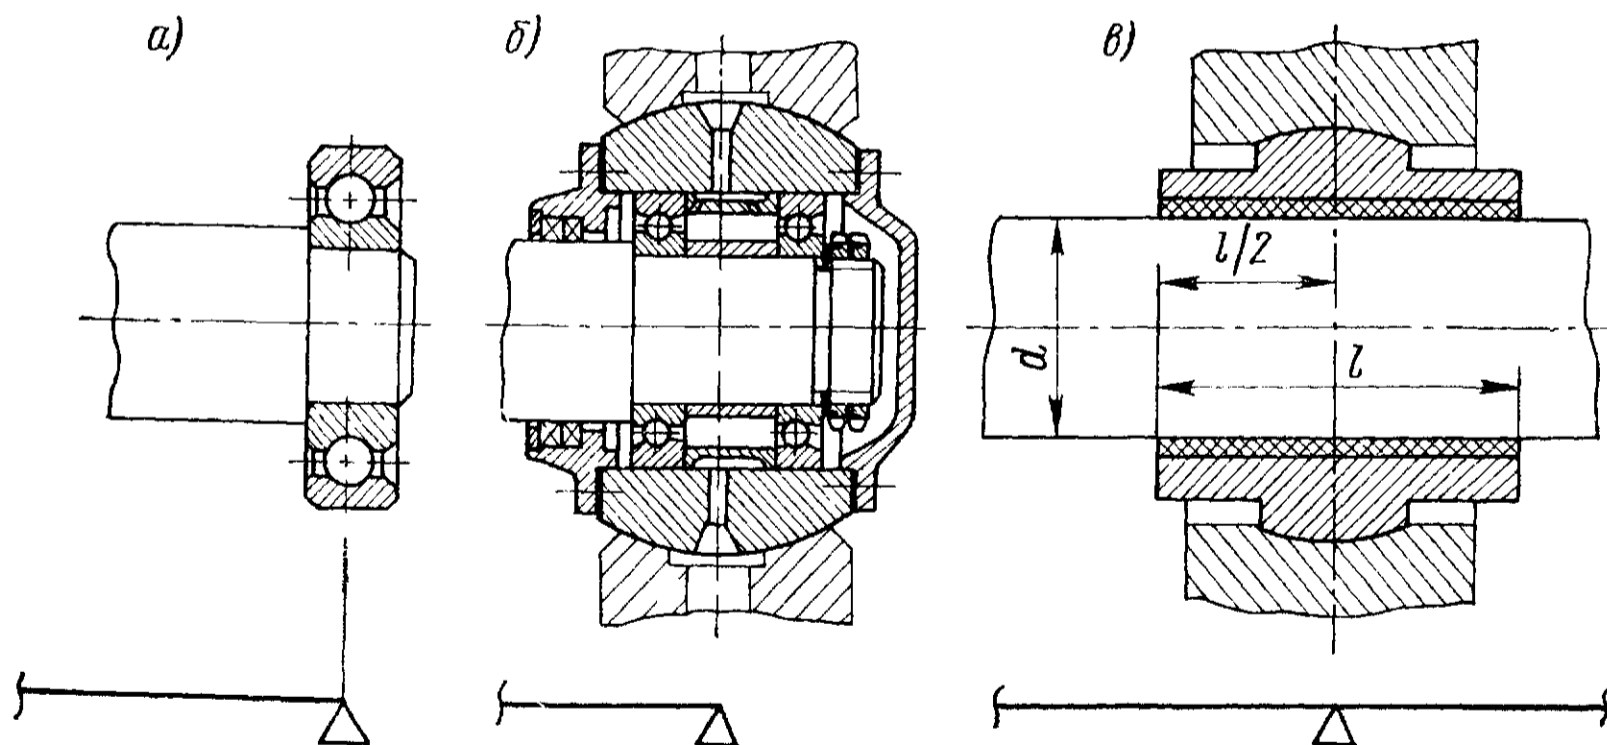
Короткие шарнирные опоры валов: а — одиночный подшипник качения; б — сдвоенные подшипники качения, размещенные в сферической самоустанавливающейся втулке; в — самоустанавливающийся подшипник скольжения
